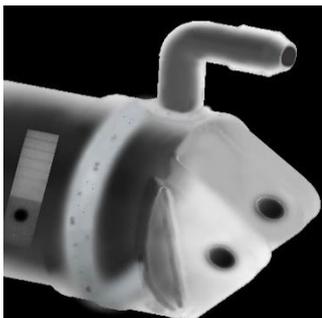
Рентгенограмма сварного шва в месте соединения цилиндра с крышкой
